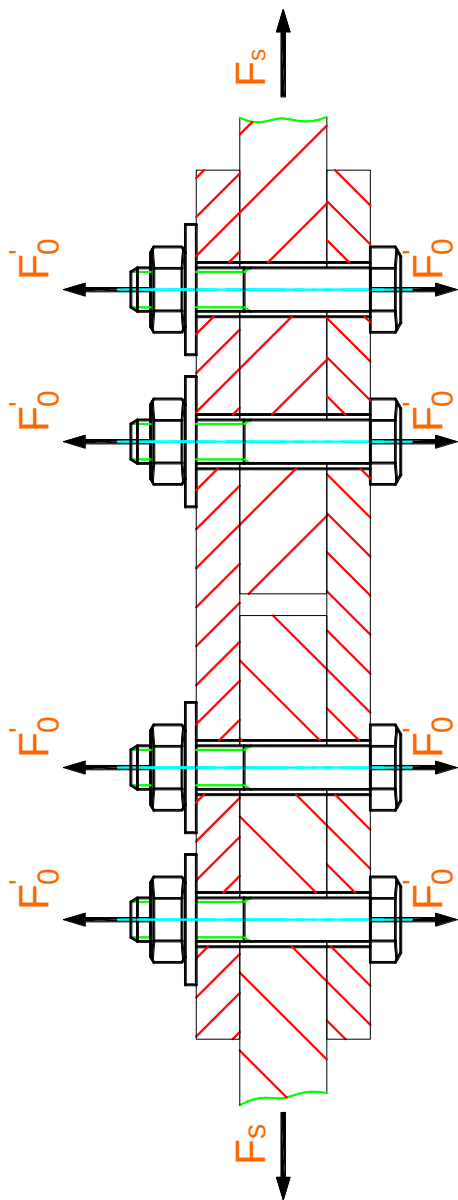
Розрахункова схема з'єднання болтами двох половин тяги
